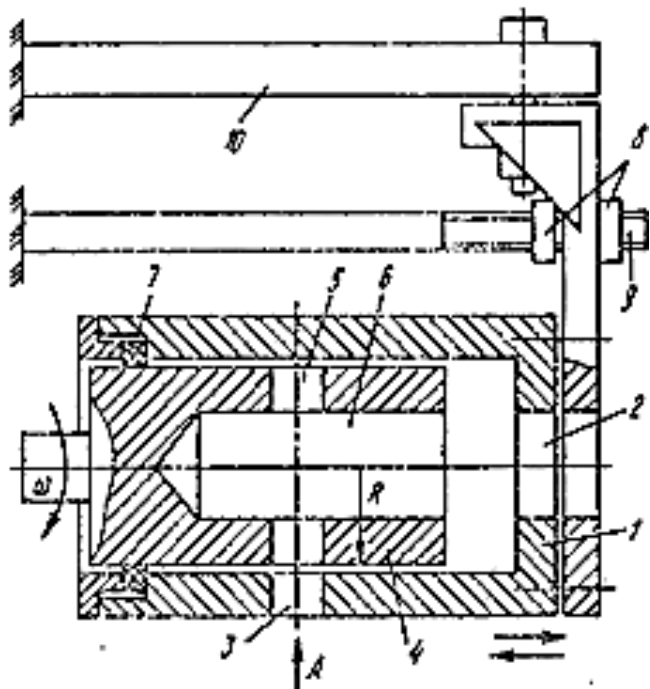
Общий вид предлагаемого устройства (в разрезе)
